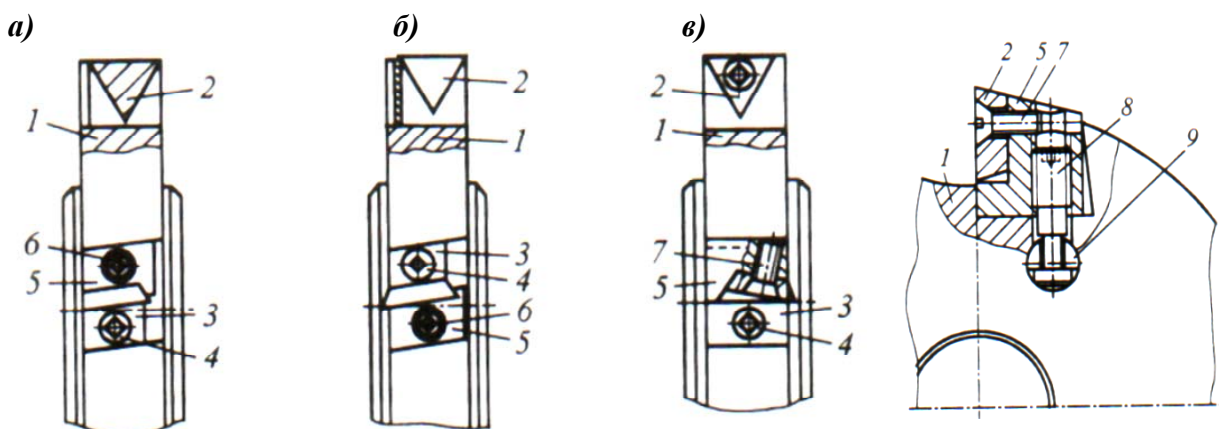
Основные конструкции сборных дисковых фрез с вкладышами для крепления СМП трехгранной формы
